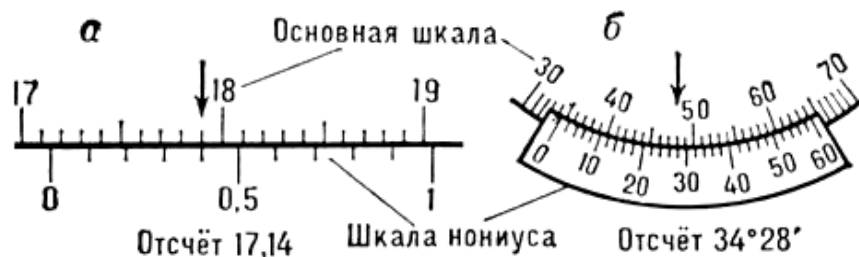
Линейный (а) и угломерный (б) нониусы.
